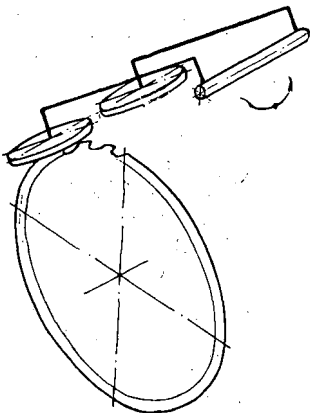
Схема шлифования боковых поверхностей зуба в станке ТчПБ-2
